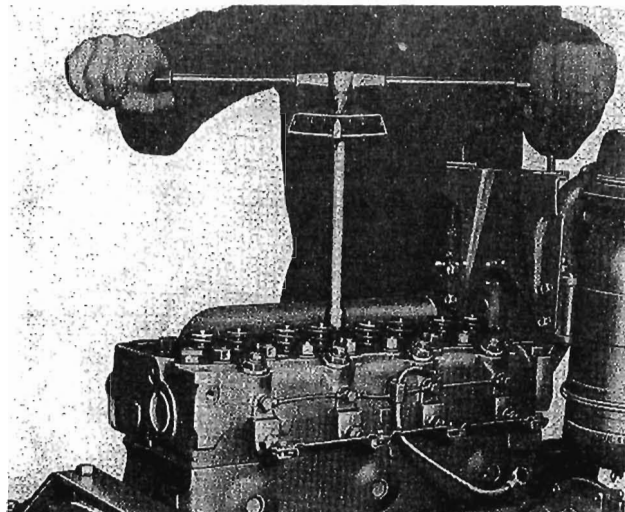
Serraggio dei dadi per testa cilindri con la chiave dinamometrica (9,5 - 10 kgm).
